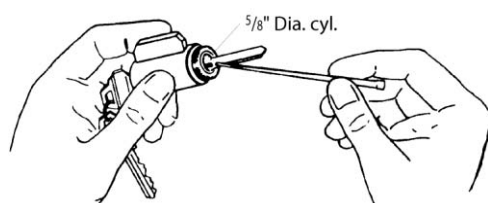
Извлеките штырь заглушки цилиндра и, провернув против часовой стрелки, вытащите ее (диаметр цилиндра 5/8 дюйма = 16 мм)
